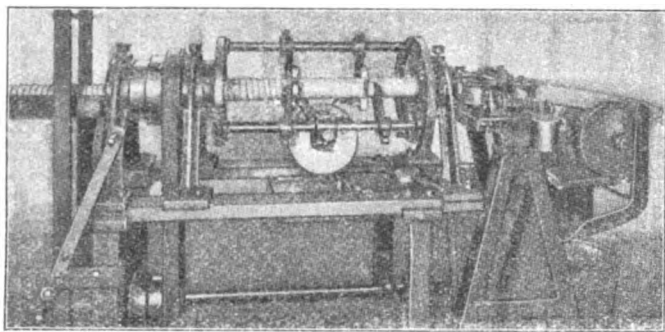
Maschine zum Umwickeln des Schlauches mit Draht.
